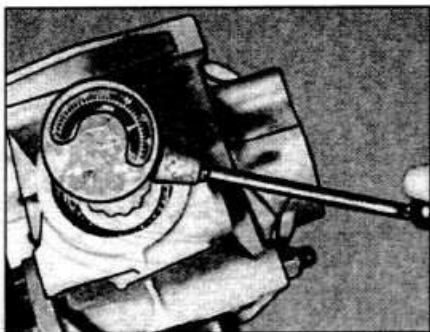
Проверка момента сопротивления проворачиванию подшипников ведущей шестерни с помощью динамометра 15.041 и втулки 15.073
